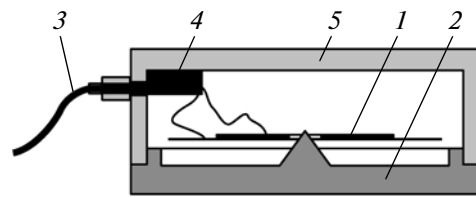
Устройство акустического датчика. 1 – биморфный пьезоэлемент, 2 – основание, 3 – кабельный ввод, 4 – предусилитель, 5 – корпус.
